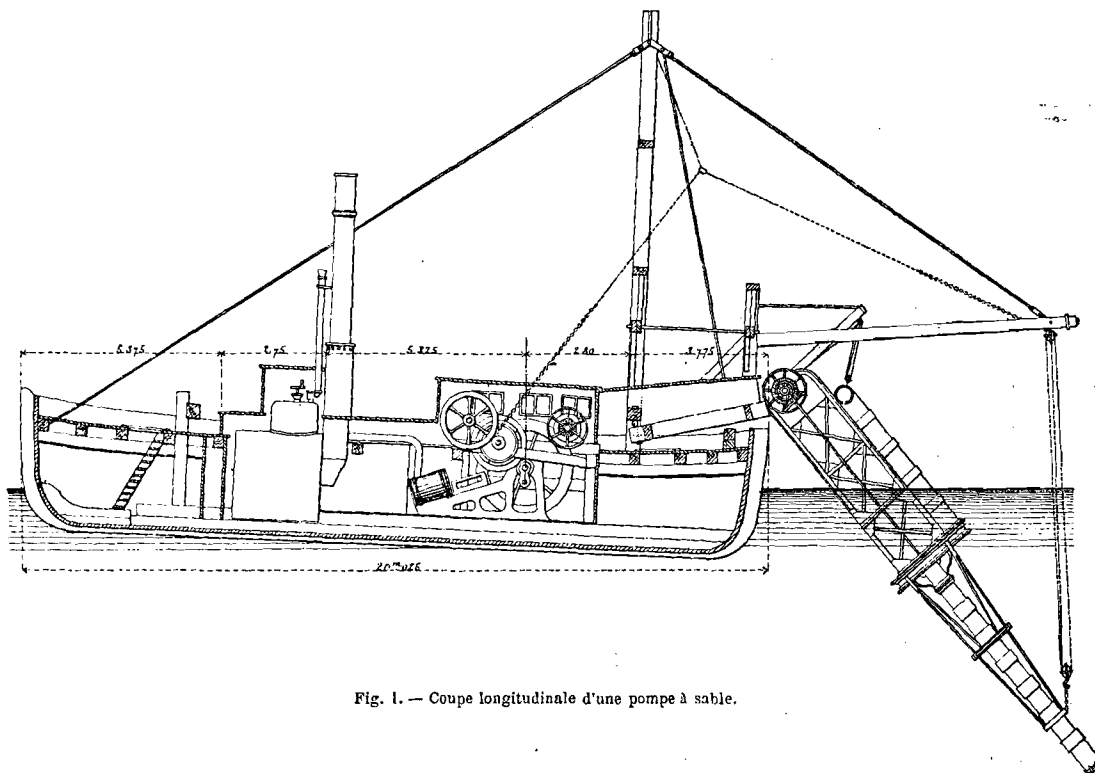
Coupe longitudinale d'une pompe à sable.
